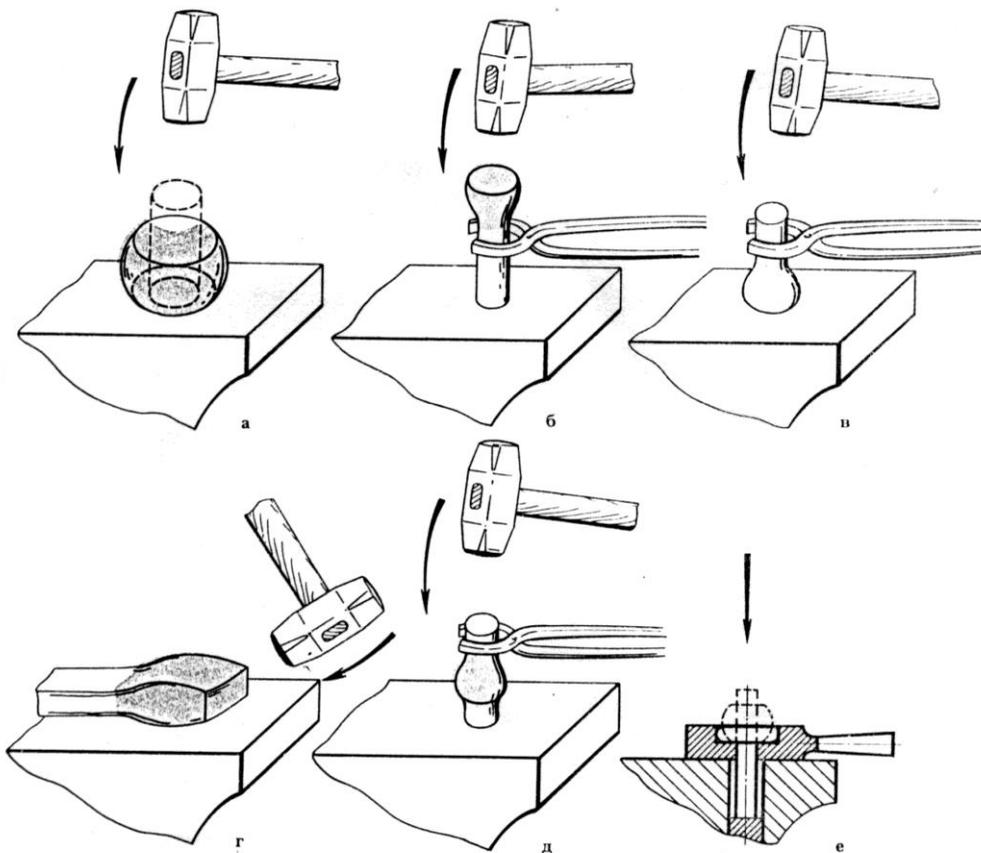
Осадка и высадка: а- осадка цилиндрической заготовки; б,в - высадка верхней и нижней частей заготовки; г – высадка конца плоской заготовки; д – высадка средней части заготовки; е – высадка головки в гвоздильне
